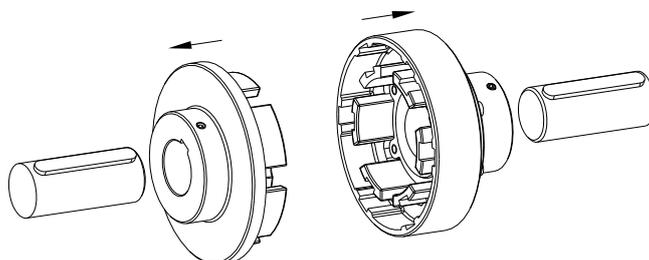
montaje de la sección de levas y manguito brida con el anillo de levas
